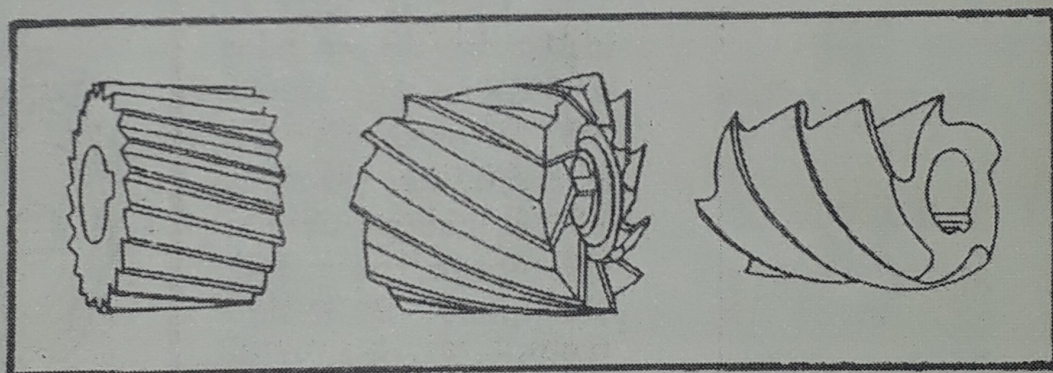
/3 (a la izquierda). — Fresa cilíndrica helicoidal de escasa inclinación.
